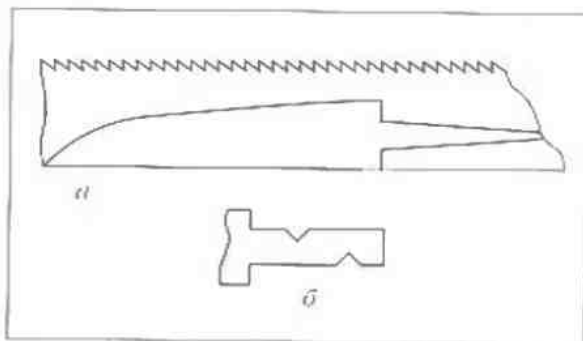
Схема изготовления ножа из полотна механической ножовки по металлу (а) и вариант хвостовика (б) (масштаб 1:2)
